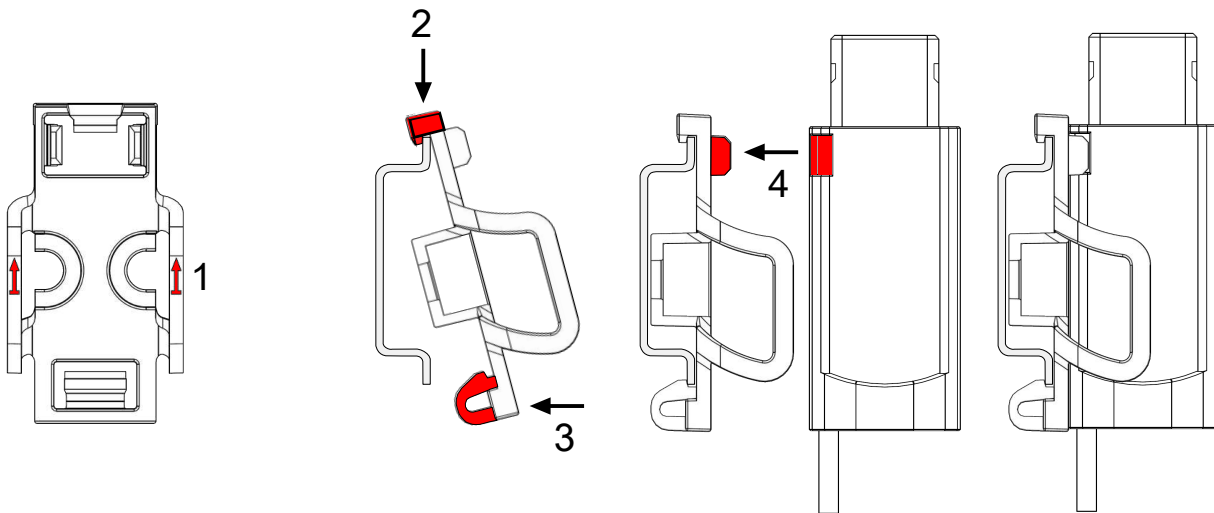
Befestigung der SCL/SVL-Wandler auf der Tragschiene mit Hilfe der Schnappbefestigung ZB8201-0900
